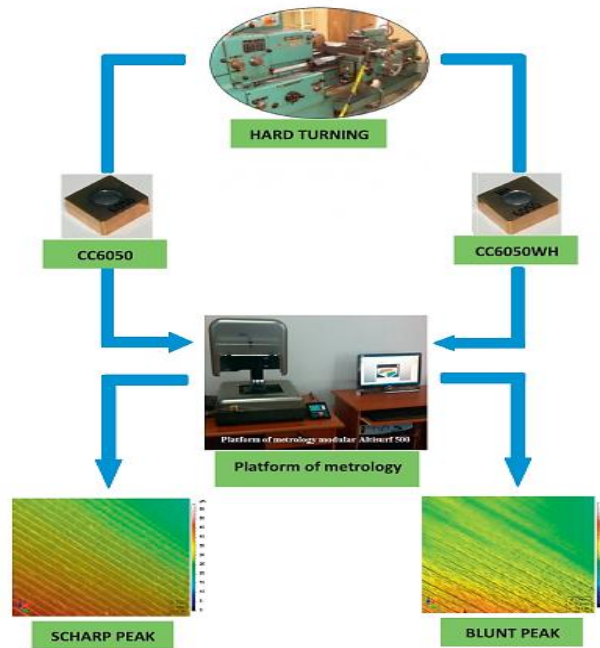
Montage expérimental pour mesurer la topographie de surface 3D des pièces.
